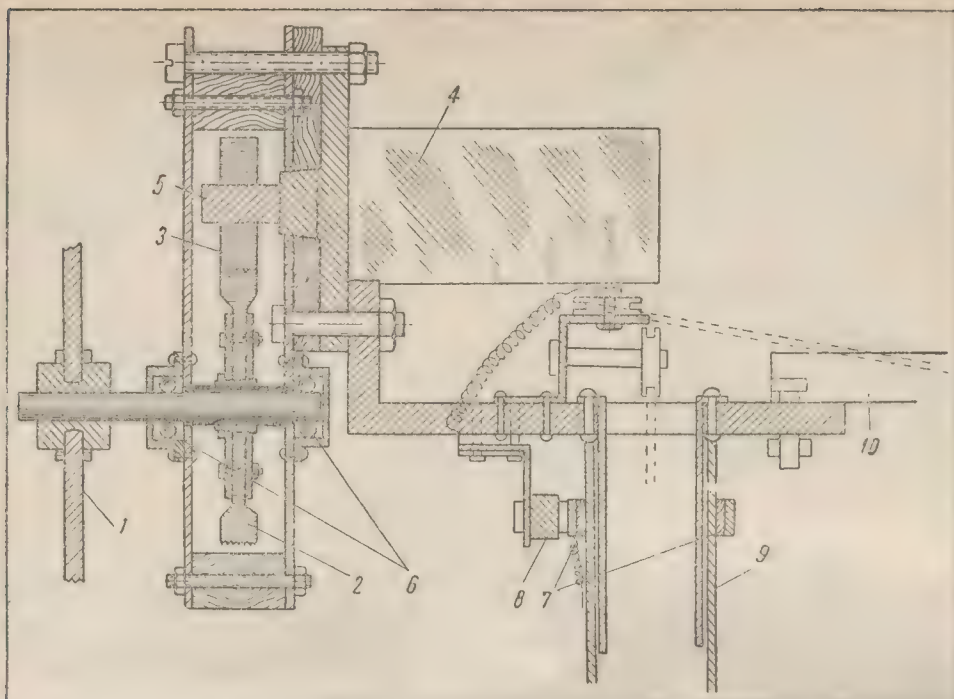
Схематический чертеж устройства ветродвигателя. 1 — винт; 2 — шестерня на валу винта; 3 — шестерня на валу динамо; 4 — динамо; 5 — вал динамо; 6 — подшипники вала винта; 7 — кольцо, изолированное от мачты; 8 — щетка, подводящая напряжение к кольцу; 9 — мачта — железная труба; 10 — хвост
